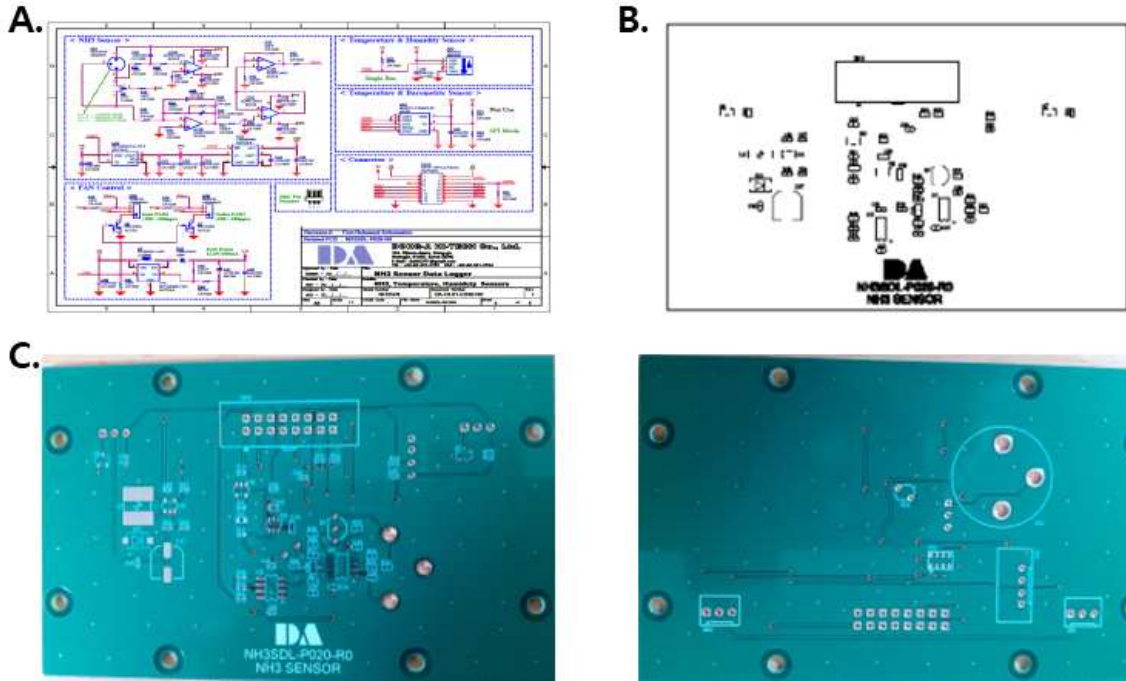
센서 파트의 PCB. (A) 센서 파트 회로도, (B) 센서 파트 거버파일, (C) 센서 파트 PCB
